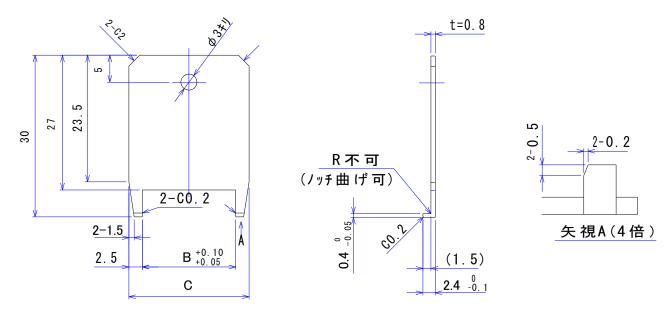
推奨抜去 JIG Recommended Plug Withdrawal Jig P/N 90466-0\*\
